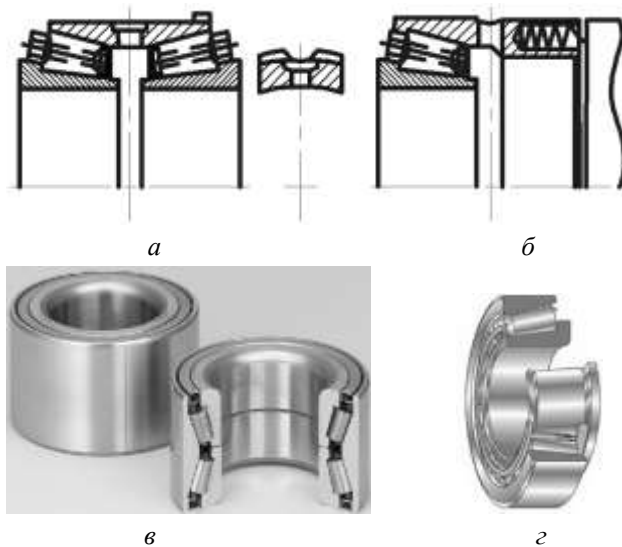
Підшипники: а, в – дворядний конічний підшипник; б, г – однорядний роликівий конічний підшипник
